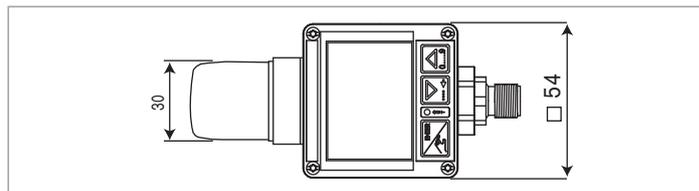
Dimensions [mm] du module électronique SE32 vu de dessus
